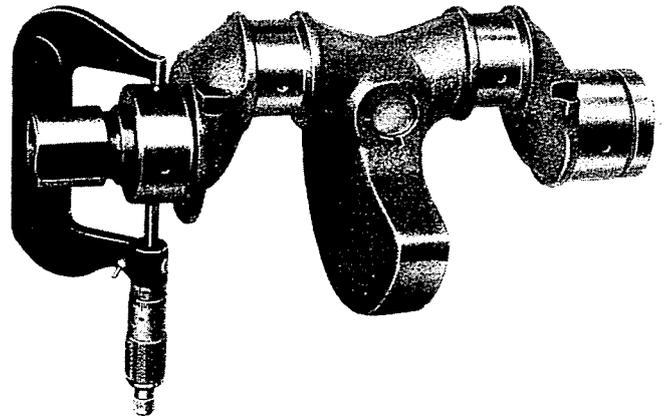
Durchmesser der Hauptlagerzapfen mit der Schraub-
